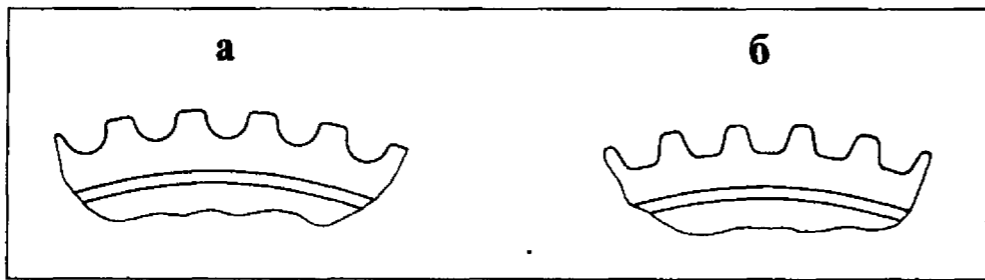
Профиль зубьев шкивов привода распределительного вала: а — шкив для ремня с полукруглыми зубьями; б — шкив для ремня с трапецевидными зубьями
